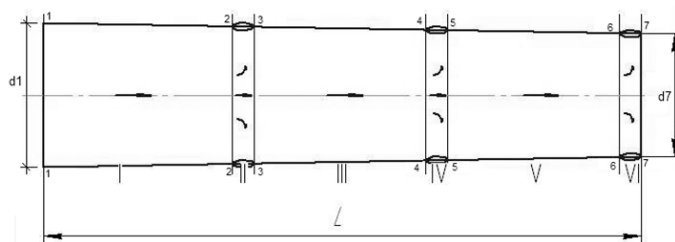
Вид конической вставки с отверстиями на боковой поверхности
